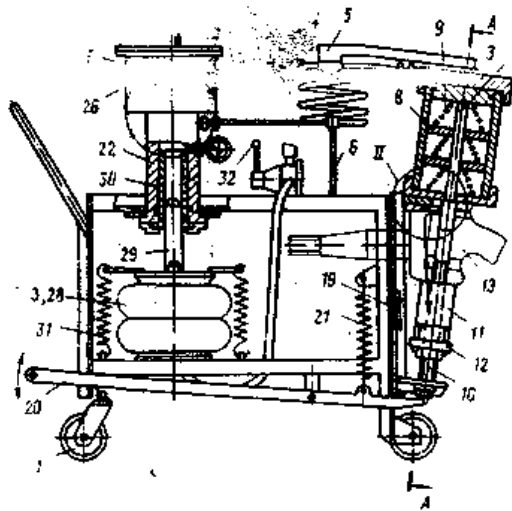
Устройство для выпрессовки шкворней поворотных цапф автотранспортных средств.
